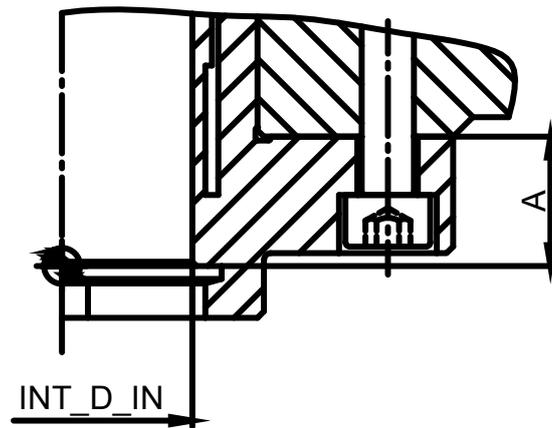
Bemaßung mit Hydrobuchse für Motoren mit Sechskant-Formschluß
